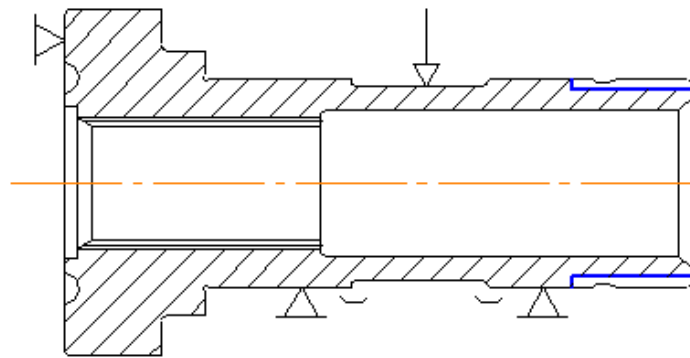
Теоретична схема базування шестірні привідної
